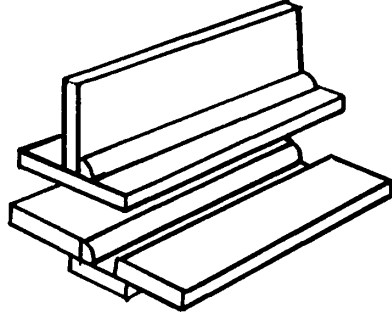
Posiciones de Ensayo para Soldaduras en planchas ranuradas (Ref.1)
